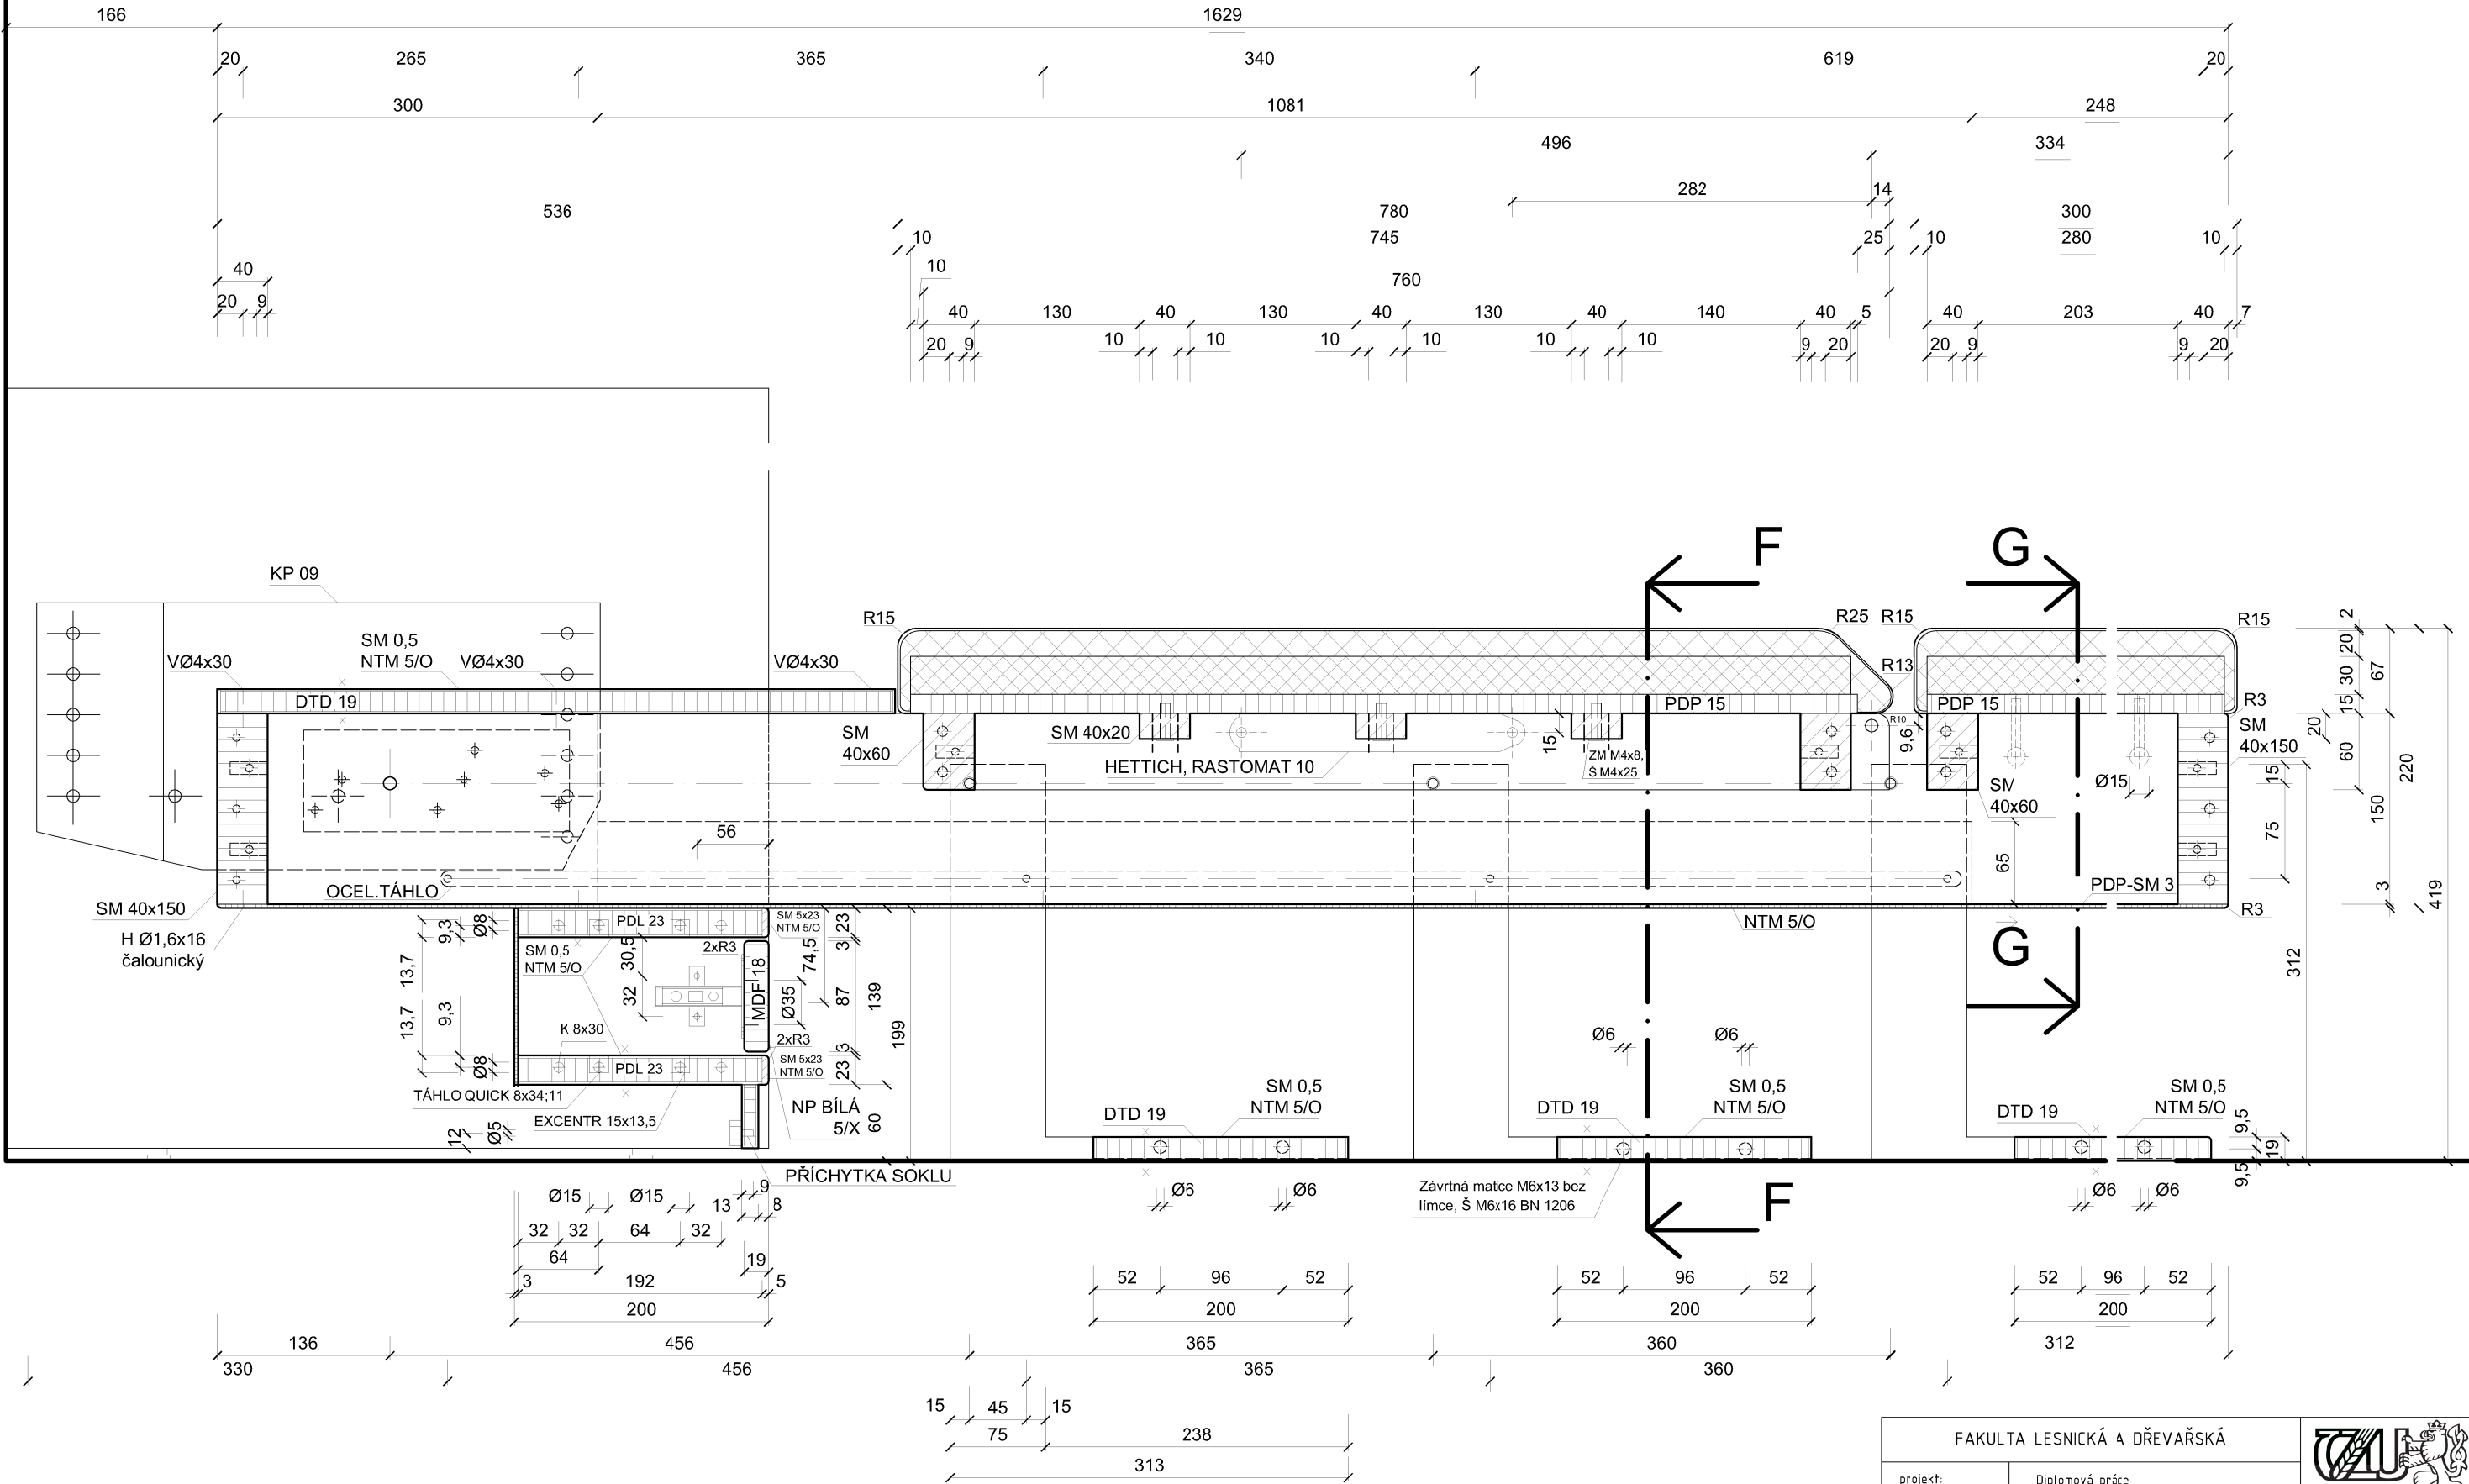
KOTVENÍ DO STĚNY 1:5
